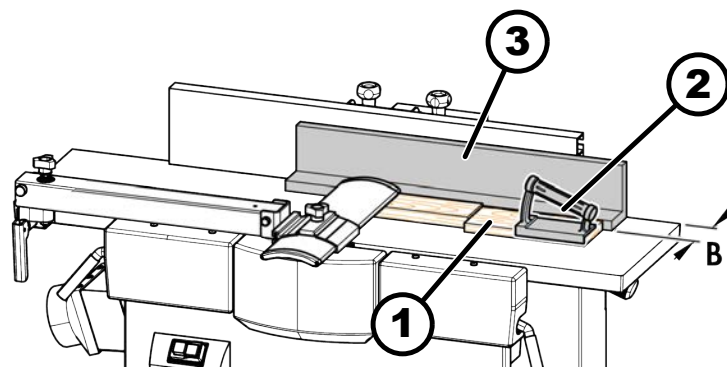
Abrichthobeln - Bearbeiten kleiner Werkstücke
